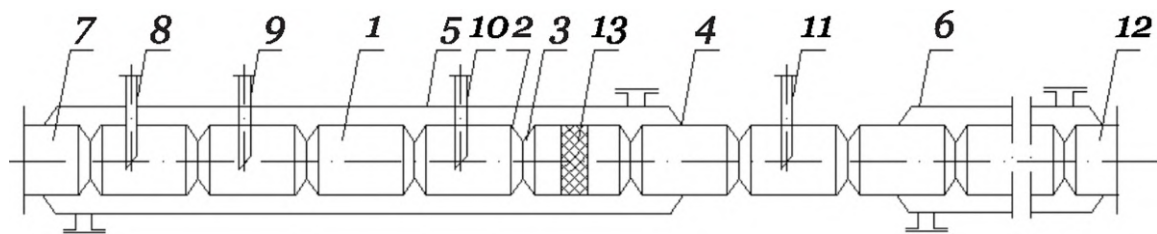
Трубчатый турбулентный аппарат диффузор-конфузорной конструкции для синтеза алкилбензола: 1 — корпус реактора; 2 — конфузорный элемент; 3 — диффузорный элемент; 4 — цилиндрический элемент; 5 — рубашка для подогрева исходной реакционной смеси; 6 — рубашка для отвода тепла реакции; 7, 8, 9, 10 — патрубки для ввода осушенного бензола, полиалкилбензолов, возвратного бензола, этилена и каталитического комплекса, соответственно; 11 — патрубок отвода реакционной смеси; 12 — патрубок отвода реакционной смеси; 13 — турбулизирующая насадка
